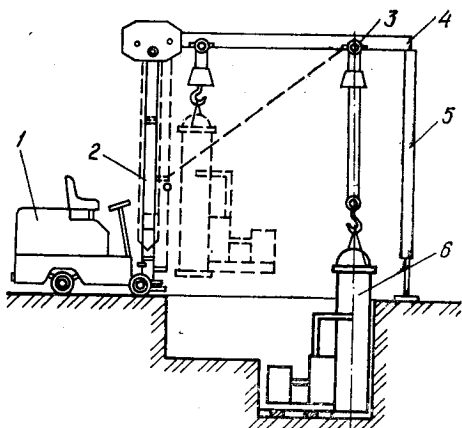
Демонтаж оборудования передвижной кран-балкой, смонтированной на базе авто- или электропогрузчика:
